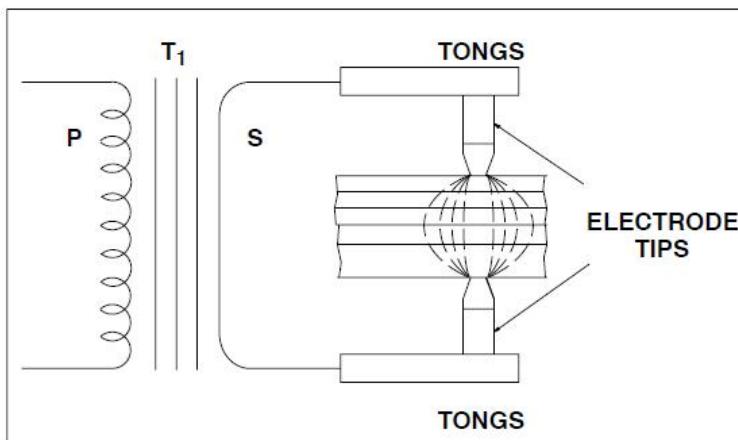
Zones thermiques de soudage par points par résistance
